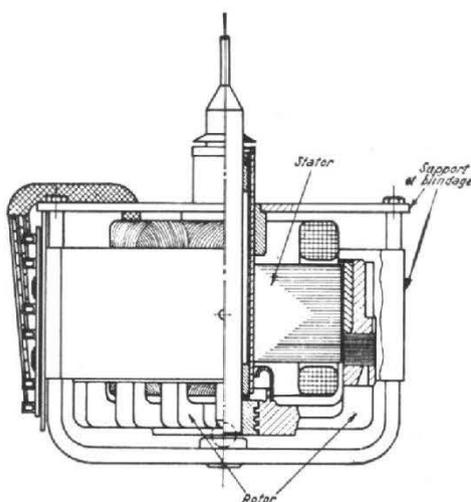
Moteur PAPST : vue en coupe du moteur représenté sur la figure 1. Le bobinage est fixe, le rotor est en forme de cloche
